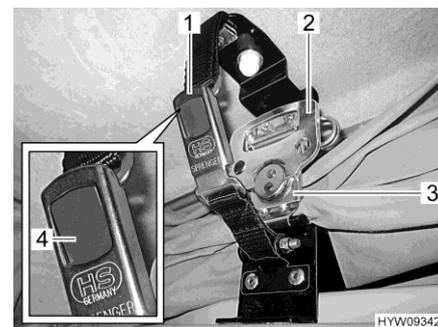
Bloccaggio, tetto a soffietto anteriore (C 500)
